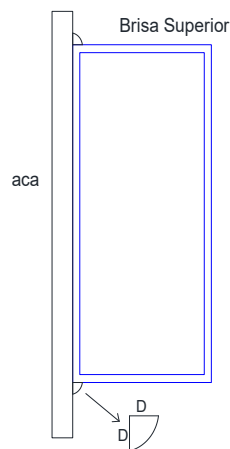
Soldadura de filete en Brida Superior
